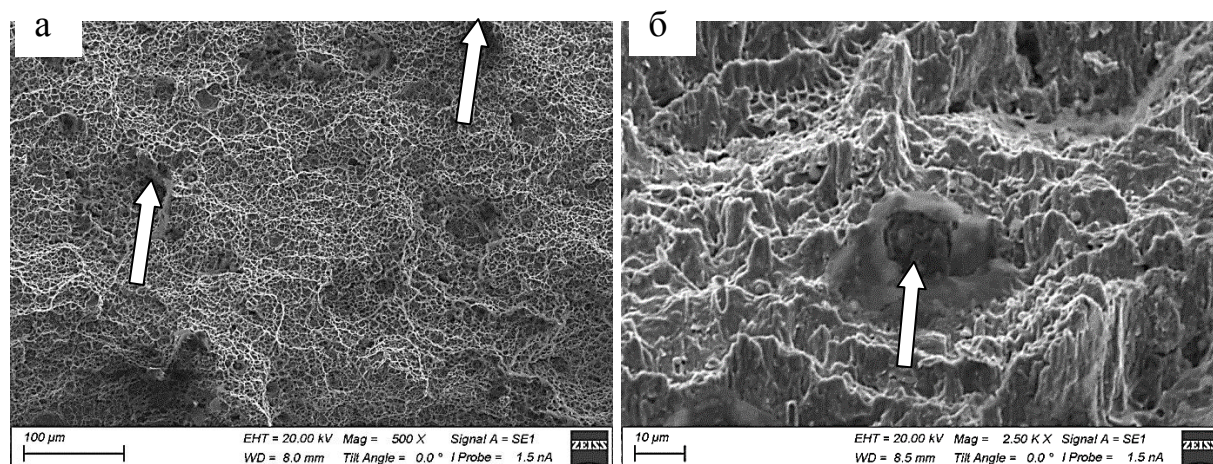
Поверхность вязкого излома металла сварного шва образца №2. Стрелками указаны неметаллические включения.
